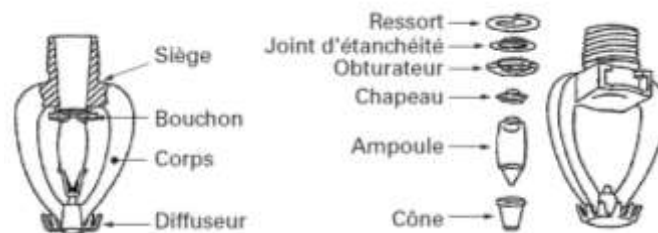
Tête de sprinklers vue éclaté [14] ; [BAD] ;
